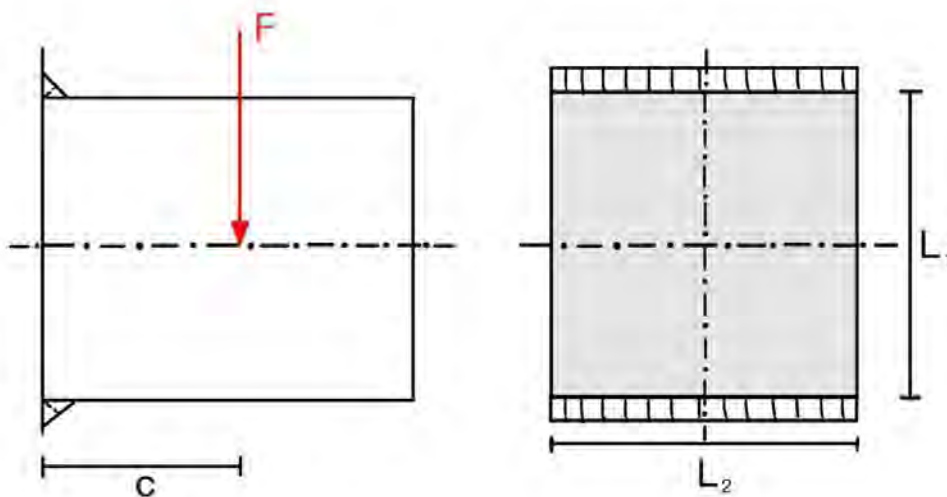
Diagrama de cordones de soldadura para carcasa electrónica. (Fuente: Elaboración propia)
